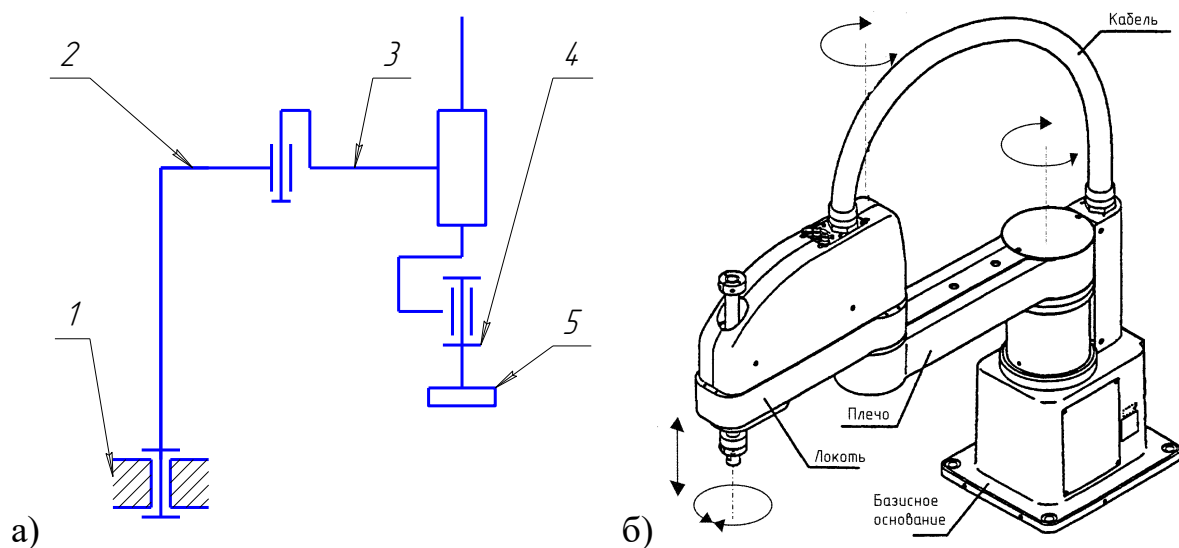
манипулятор СКАРА: а – кинематическая схема; б – внешний вид
